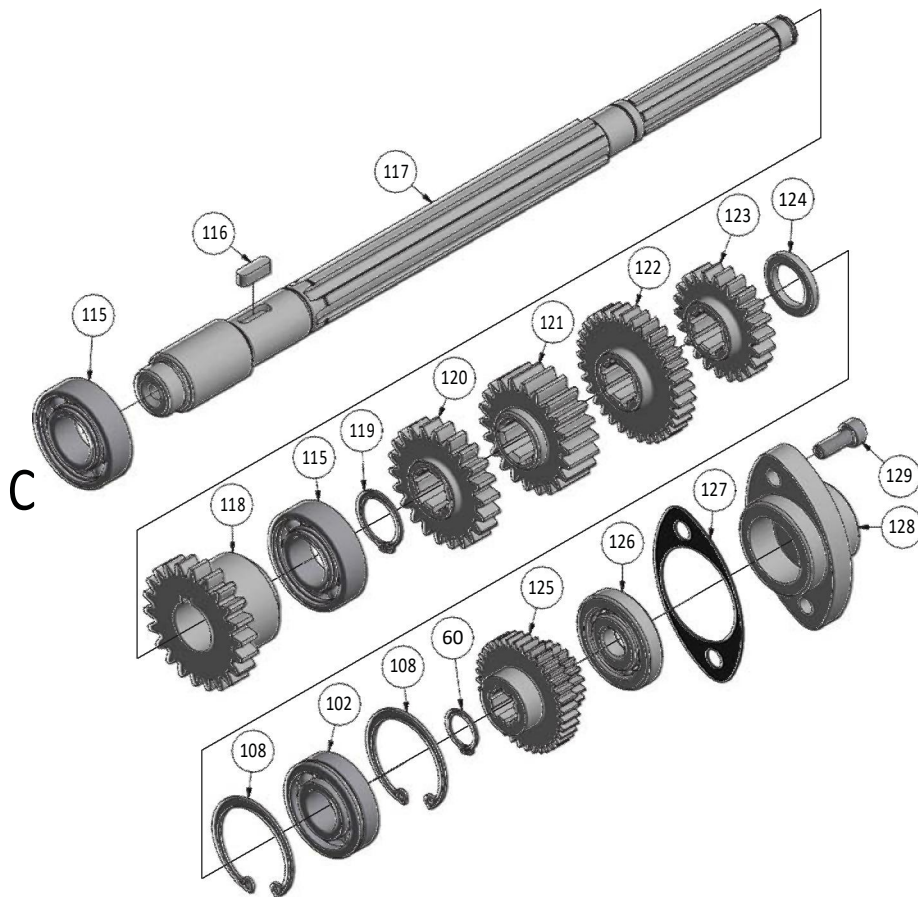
Vorschubgetriebe 5-9 –Engranaje de avance 5-9
